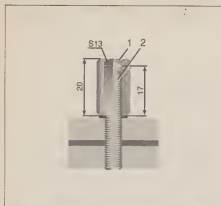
Колпачковая гайка 1 на шпильке 2 коллектора.
